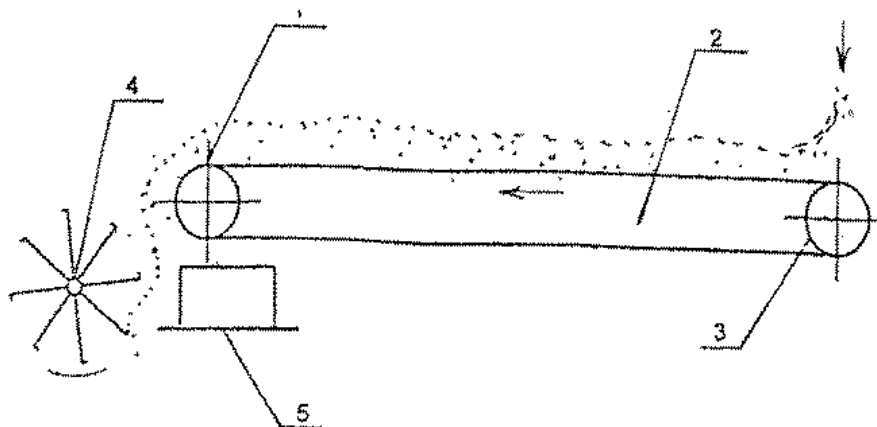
Схема установки лопастного колеса в зоне разгрузки конвейера 1- приводной барабан; 2- транспортерная лента конвейера; 3- натяжной барабан; 4- лопастное колесо (вал с лопастями); 5- рама приводного барабана.
